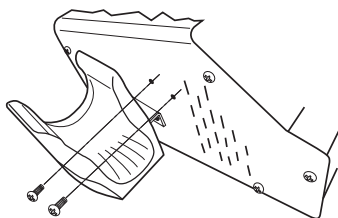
Instale o estojo do soldador de ar quente
